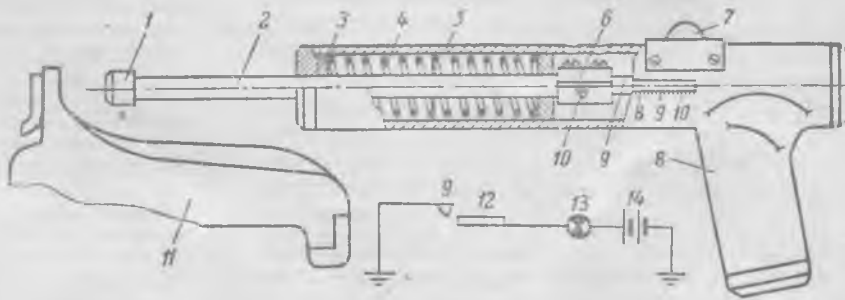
Динамометр для измерения нажатия контактов ПКГ электровозов серий ЧС: 1 — резиновый упор; 2 — стержень; 3 — нажимная шайба; 4 — пружина; 5 — ствол; 6 — муфта; 7 — плафон сигнальной лампы; 8 — рукоятка; 9 — подвижной контакт; 10 — указатель; 11 — подвижной контакт контактора ПКГ; 12 — контакт; 13 — сигнальная лампа; 14 — элементы 1,6-ФМЦ-У-3,2
